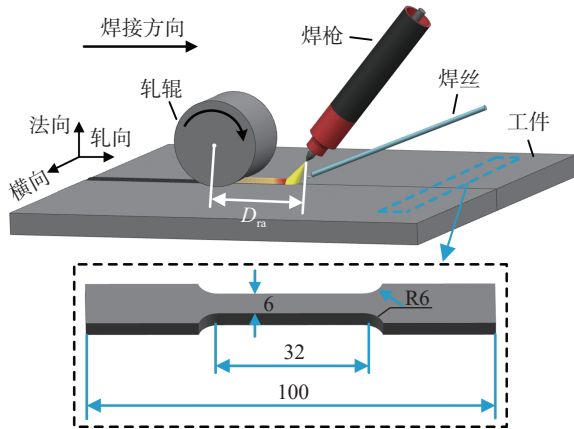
随焊碾压系统示意图及拉伸试样尺寸 (mm)
